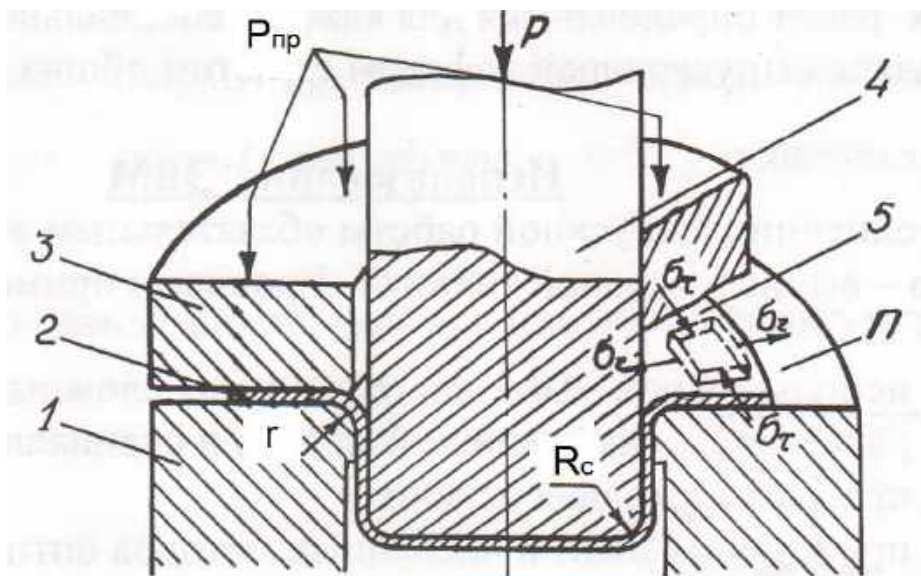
Принципова схема витяжки: 1 – матриця; 2 – заготовка; 3 – притискач; 4 – пуансон; 5 – фланець заготовки; П – протяжна поверхня матриці; r – радіус перетяжного ребра матриці; R_c – радіус скруглення пуансона; P – зусилля витяжки; $P_{пр}$ – зусилля притискання
